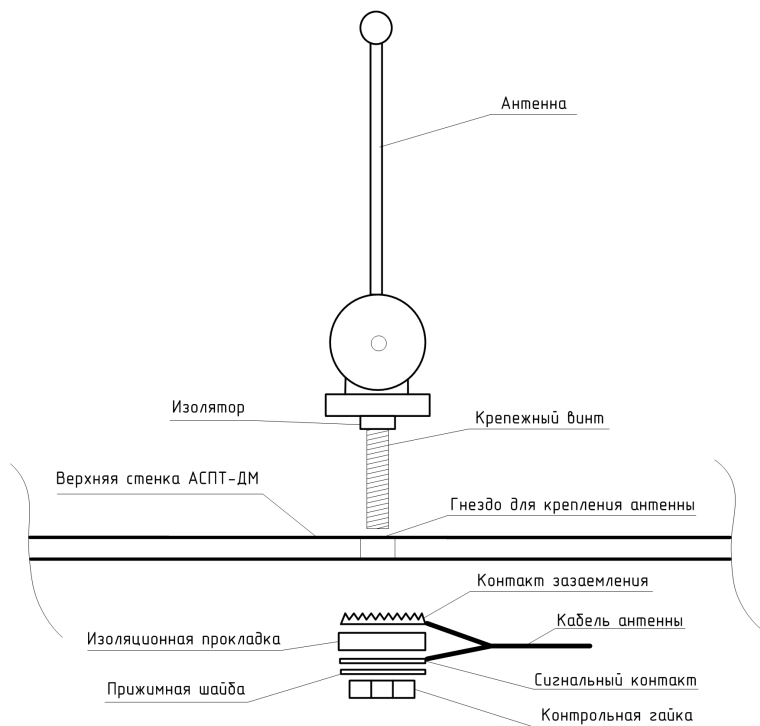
Схема крепления антенны к корпусу АСПТ-ДМ
